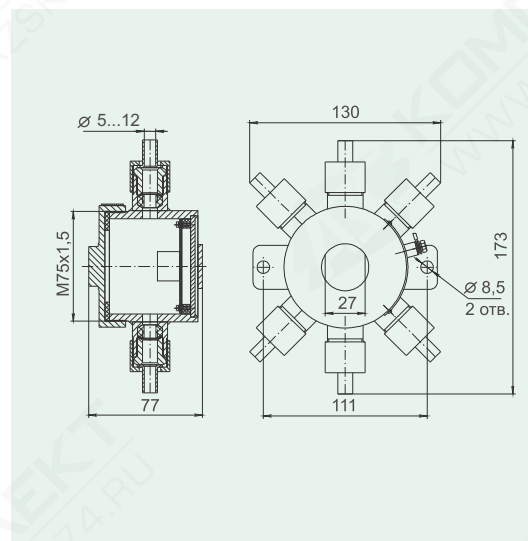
Коробка ВУУК. Габаритные и установочные размеры.
